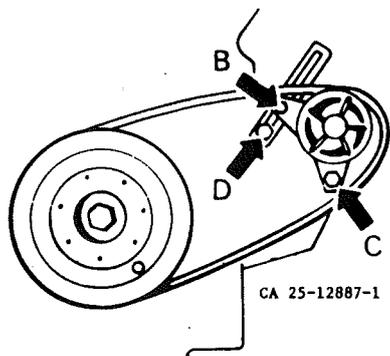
Tensione della cinghia trapezoidale (alternatore)
